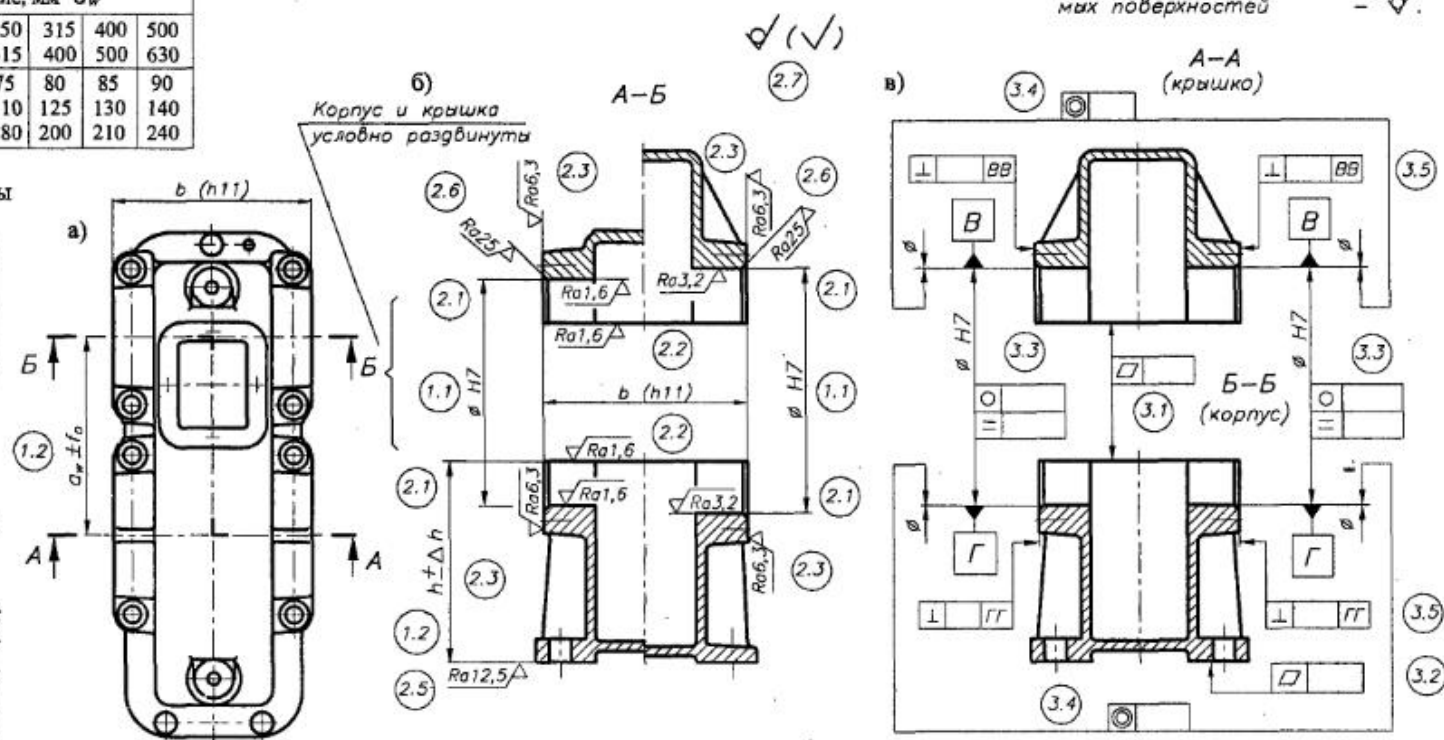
Обозначение на корпусных деталях редукторов:
